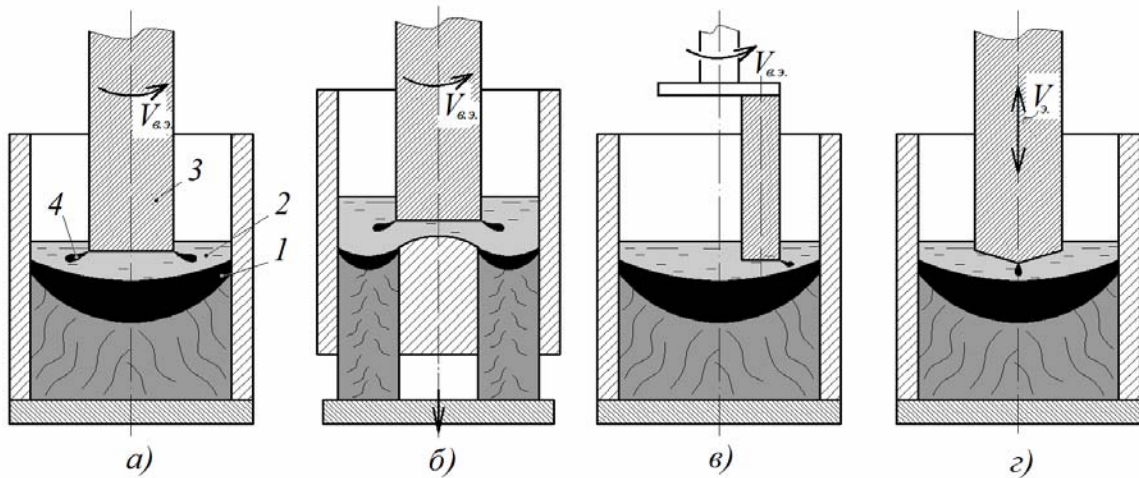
Схеми ЕШП з обертанням (а-в) і зворотно-поступальним переміщенням (г) витратного електроду: 1 - металева ванна; 2 – шлакова ванна; 3 – витратний електрод; 4 – крапля електродного металу.
